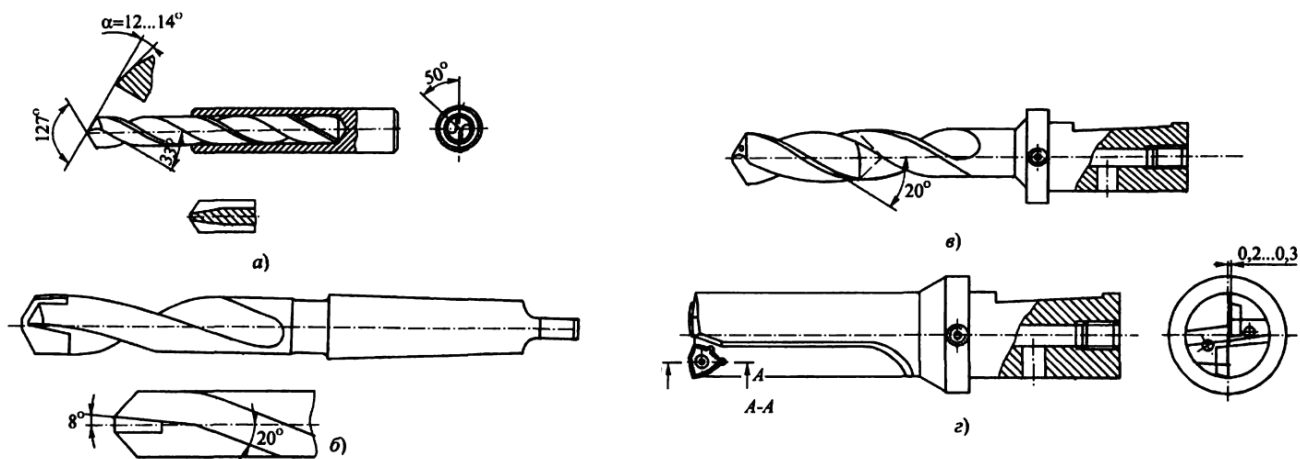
Твердосплавные сверла: а – цельные; б – с напайными пластинами; в – с коронками; г – с механическим креплением СМП
